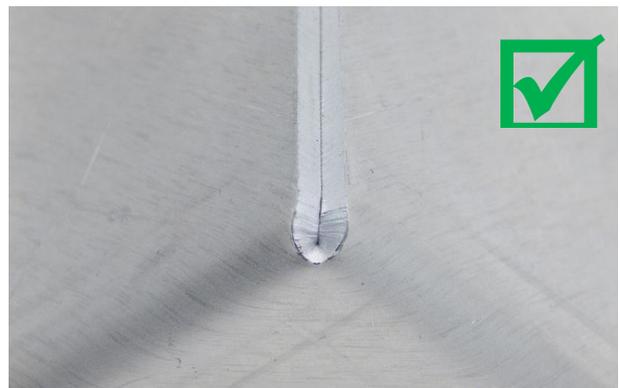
Biegeauge Aluminium t = 2,5 mm
